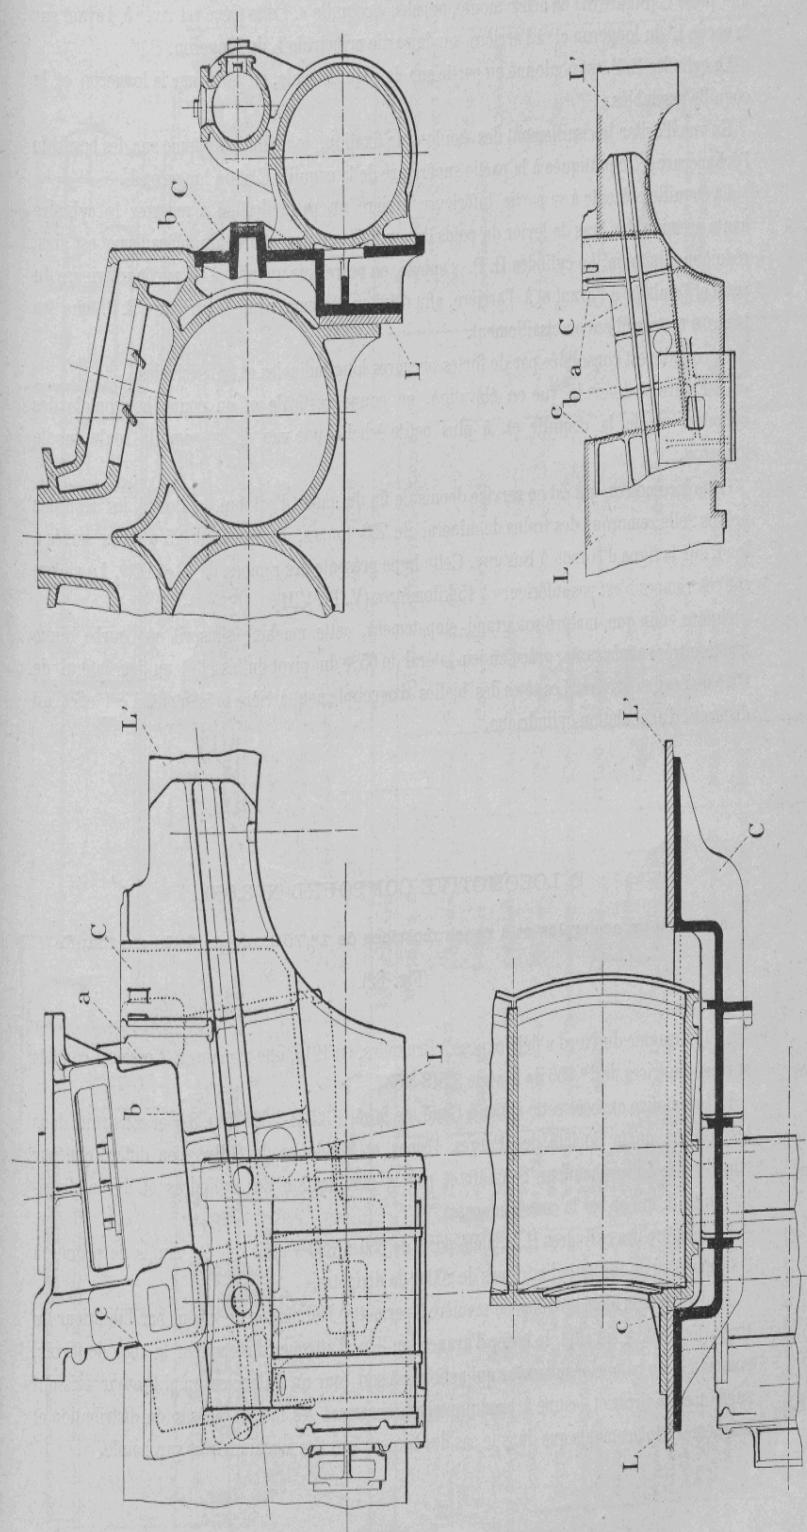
Coquille d'assemblage du cylindre B. P.
